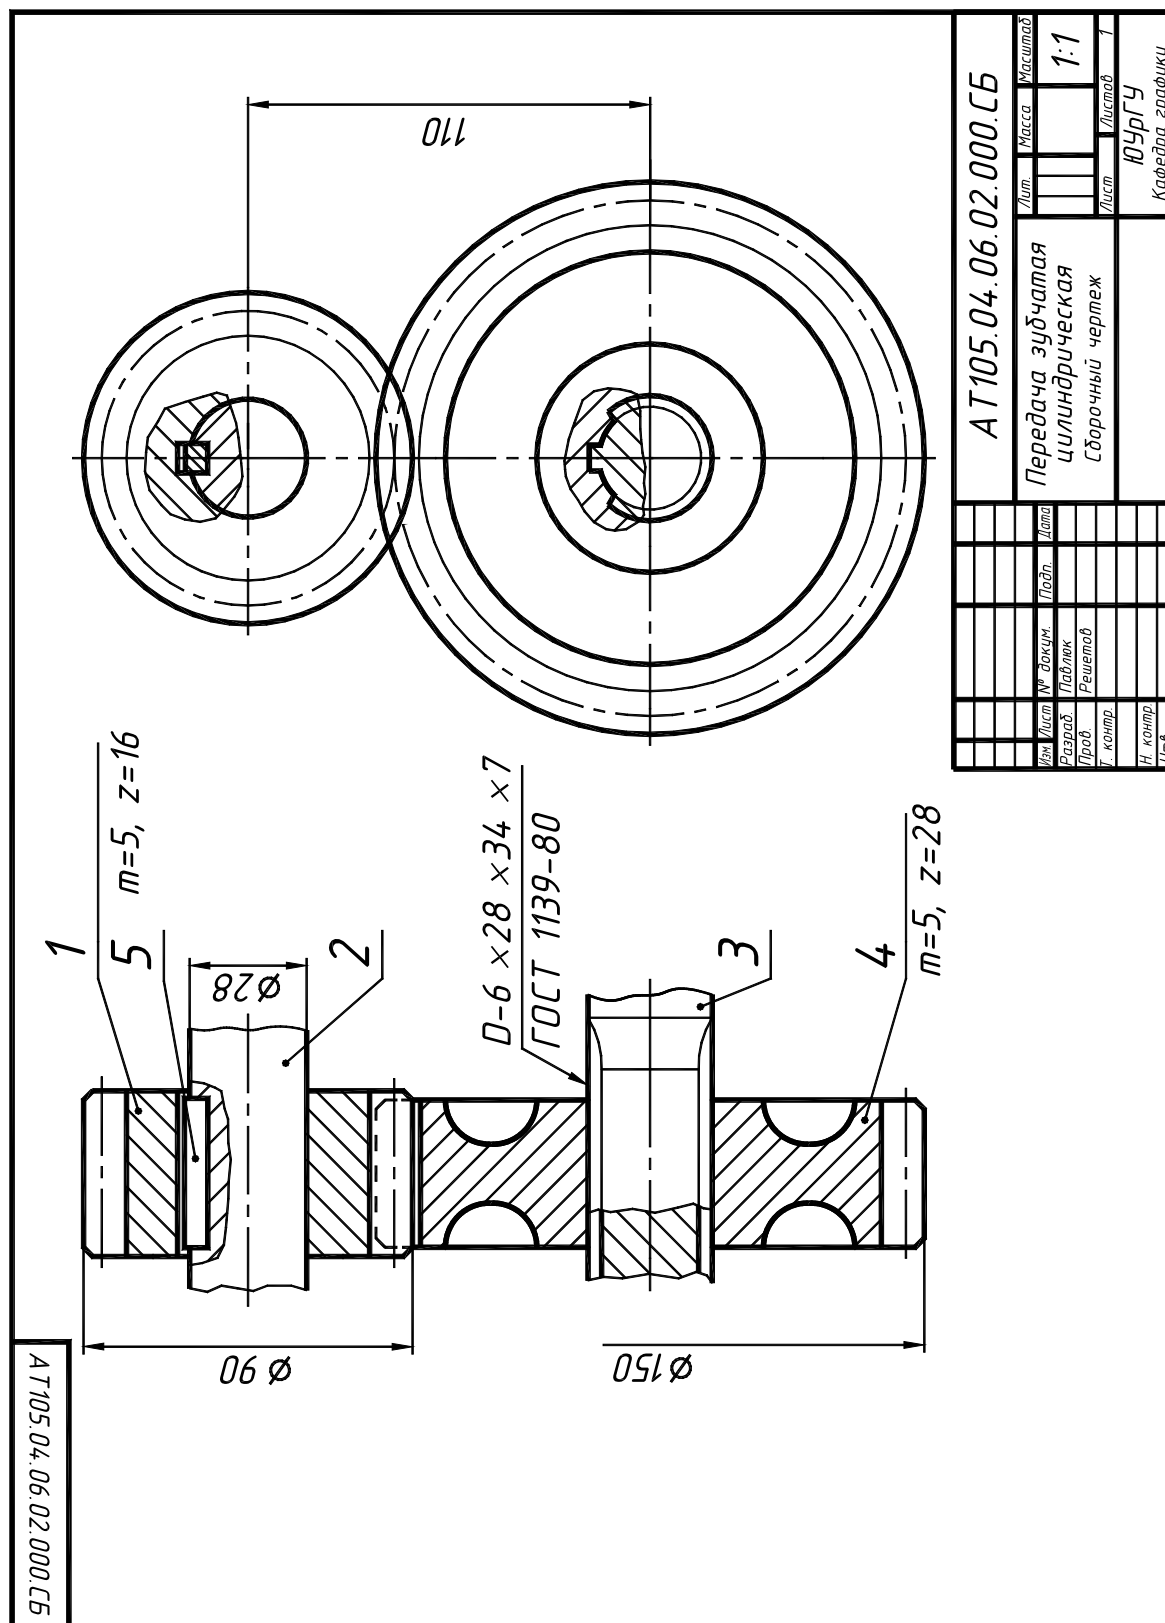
Пример выполнения чертежа передачи зубчатой цилиндрической
